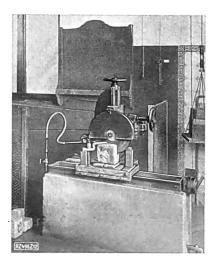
Maschine für die Bearbeitung von Natursteinen
